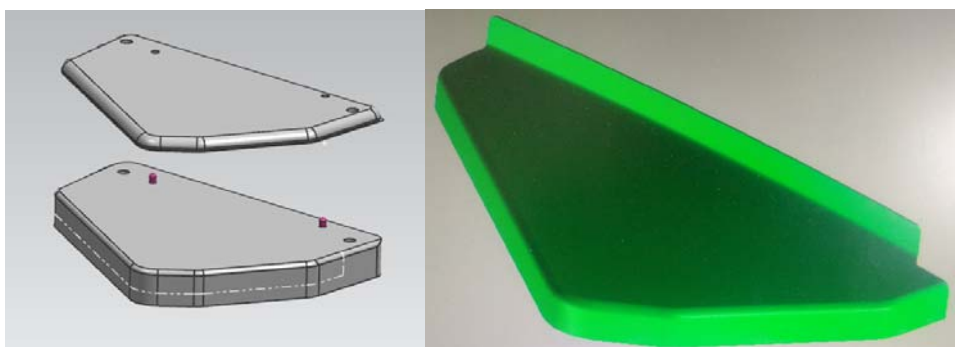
Общий вид формблока для формообразования, общий вид листовой детали
